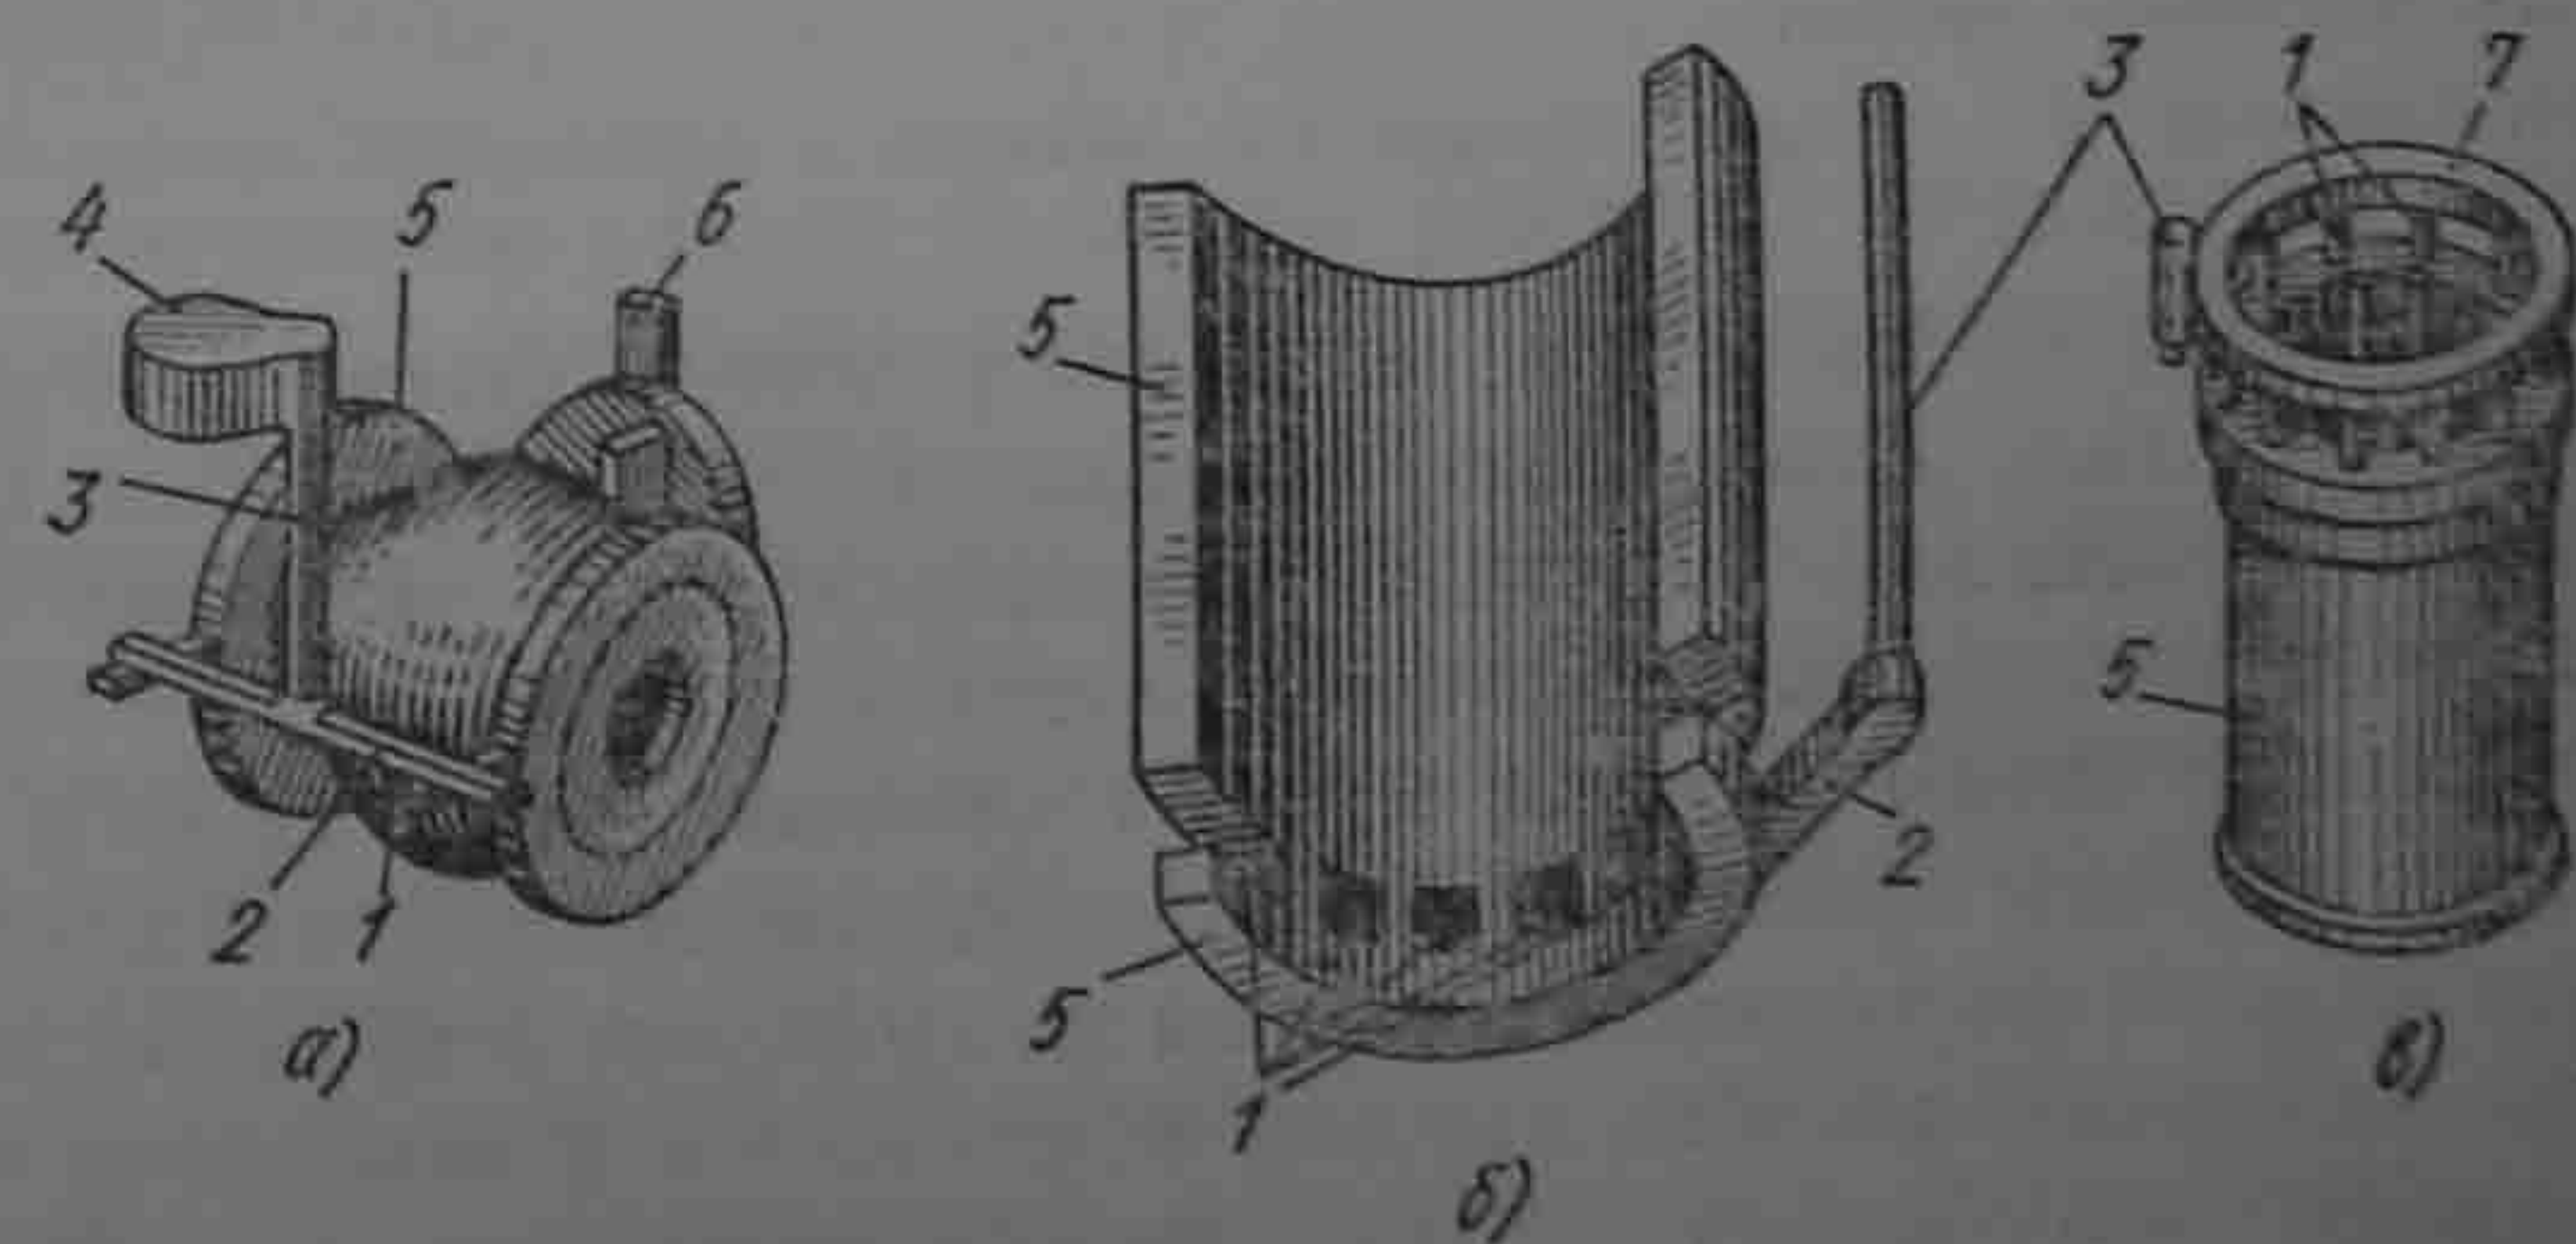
Типовые литниковые системы: а — подвод металла сбоку; б — подвод металла снизу; в — подвод металла сверху
